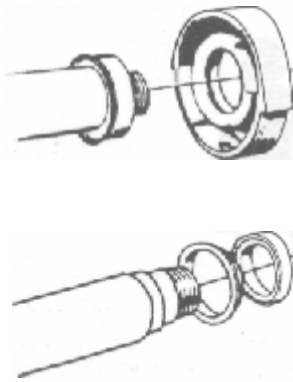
Разборка промежуточного подшипника и пылезащитной крышки — 240
